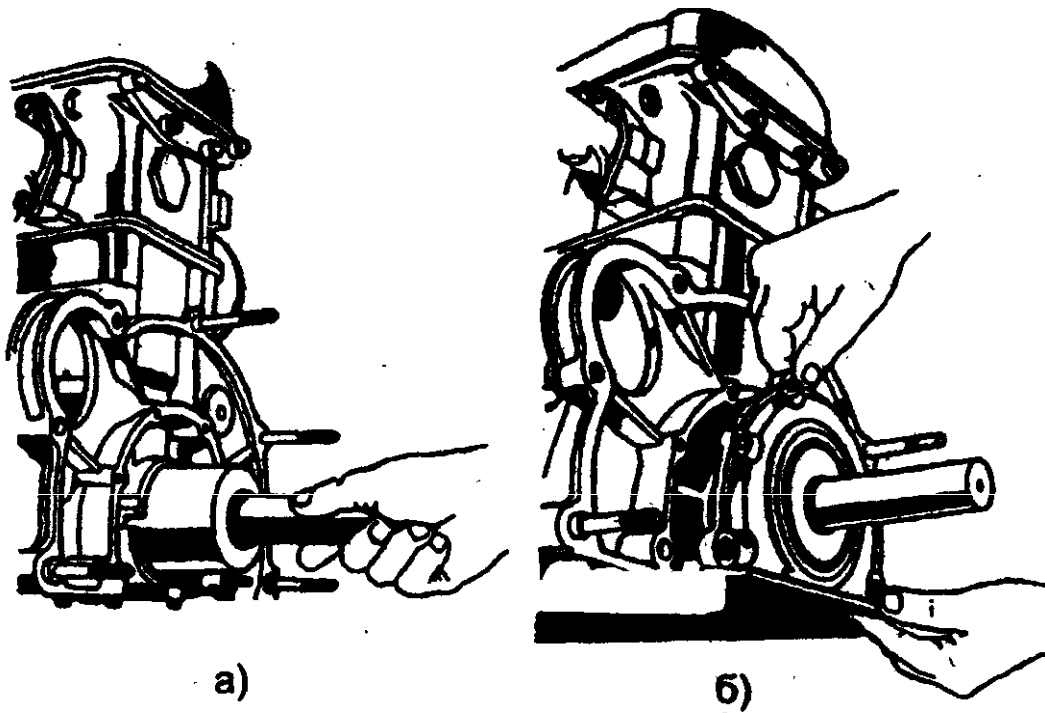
Установка крышки задней манжеты двигателя с помощью оправки:
